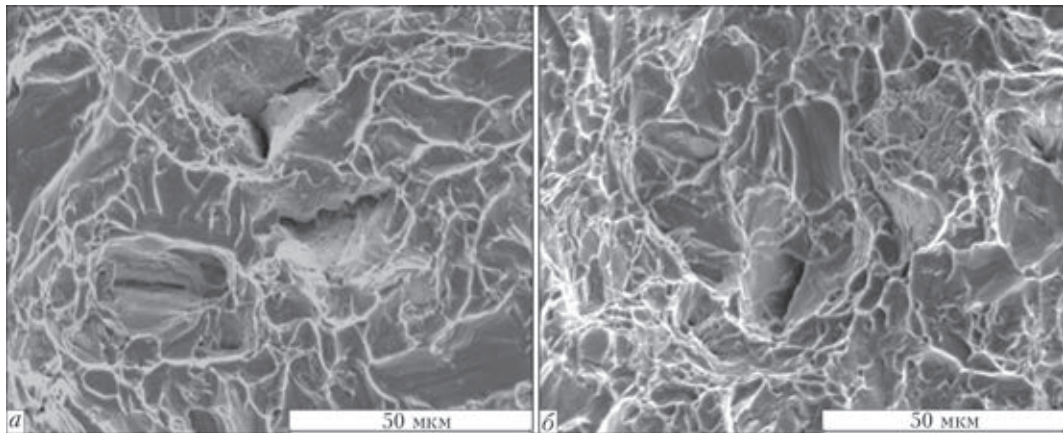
Фрактограммы поверхностей разрушений после испытаний на статическое растяжение: *a* — образца сварного соединения 1; *б* — образец 2 сварного соединения сплава технического титана BT1-0 ДШП толщиной 12 мм, упрочненного азотом (0,098 мас. %)
